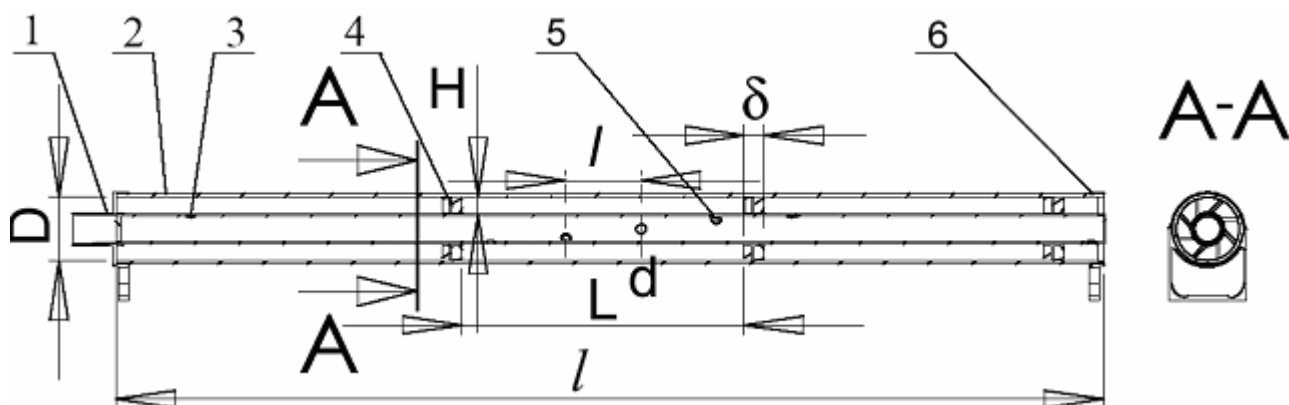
Конструкция и основные параметры физической модели «струйно-вихревого» рекуператора [84]: 1 — входная крышка с боковым патрубком для одновременной подачи дыма и воздуха и подставкой; 2 — наружная труба; 3 — перфорированная внутренняя вставка; 4 — модель лопасти в форме винтовой крыльчатки; 5 — сопло; 6 — выходная крышка с подставкой.
